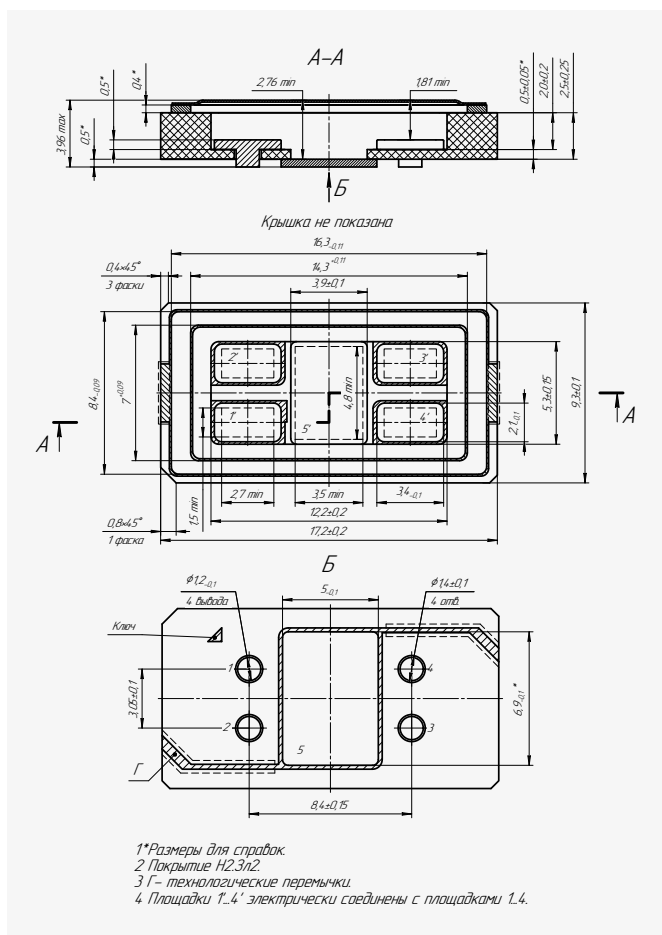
Габаритный чертёж металлокерамического корпуса КТ-118-1
